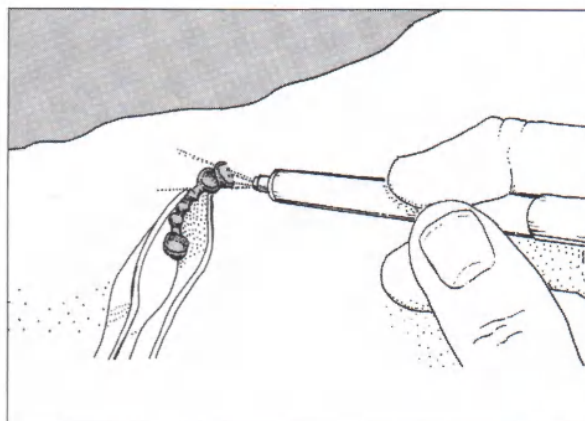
Проводят пескоструйную очистку поверхности отливки частицами оксида алюминия
